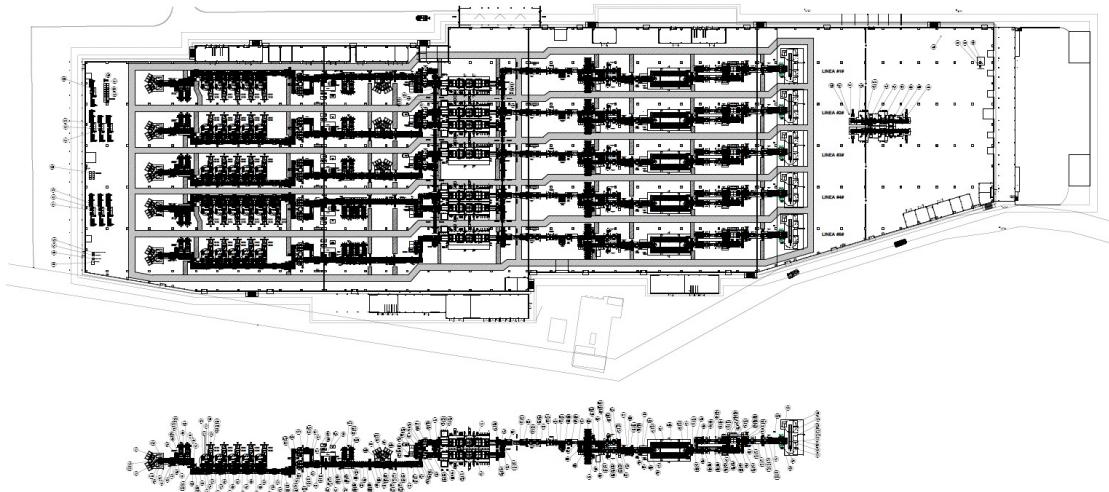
Layout impianto produzione di pannelli fotovoltaici
